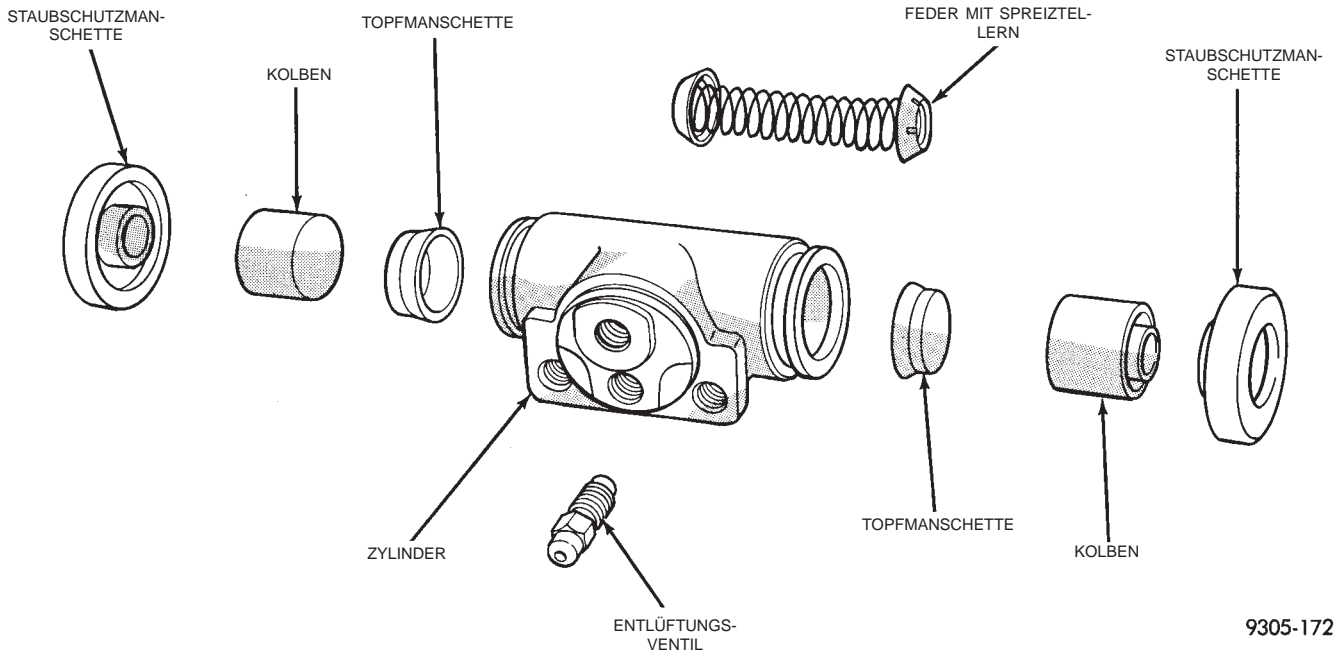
Hinterradzylinder (Explosionsdarstellung)
